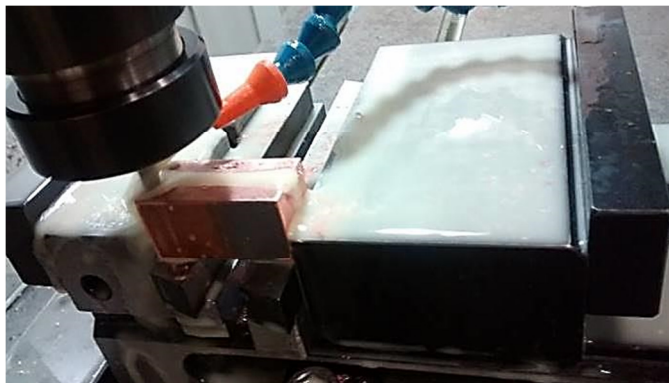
Fabricação do eletrodo ferramenta auxiliada por sistema CAD/CAM/CNC
